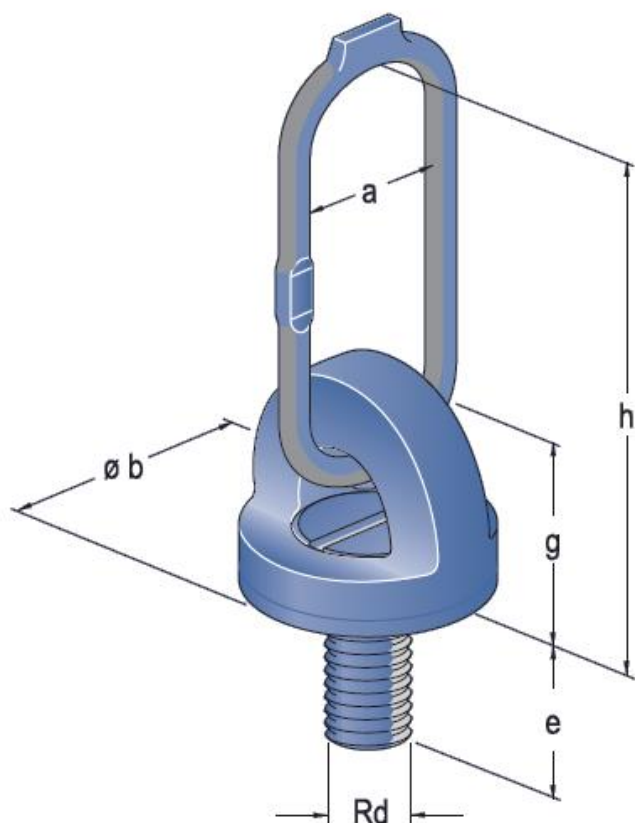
Полностью металлическое подъёмное приспособление, оборудованное прижимной деталью
